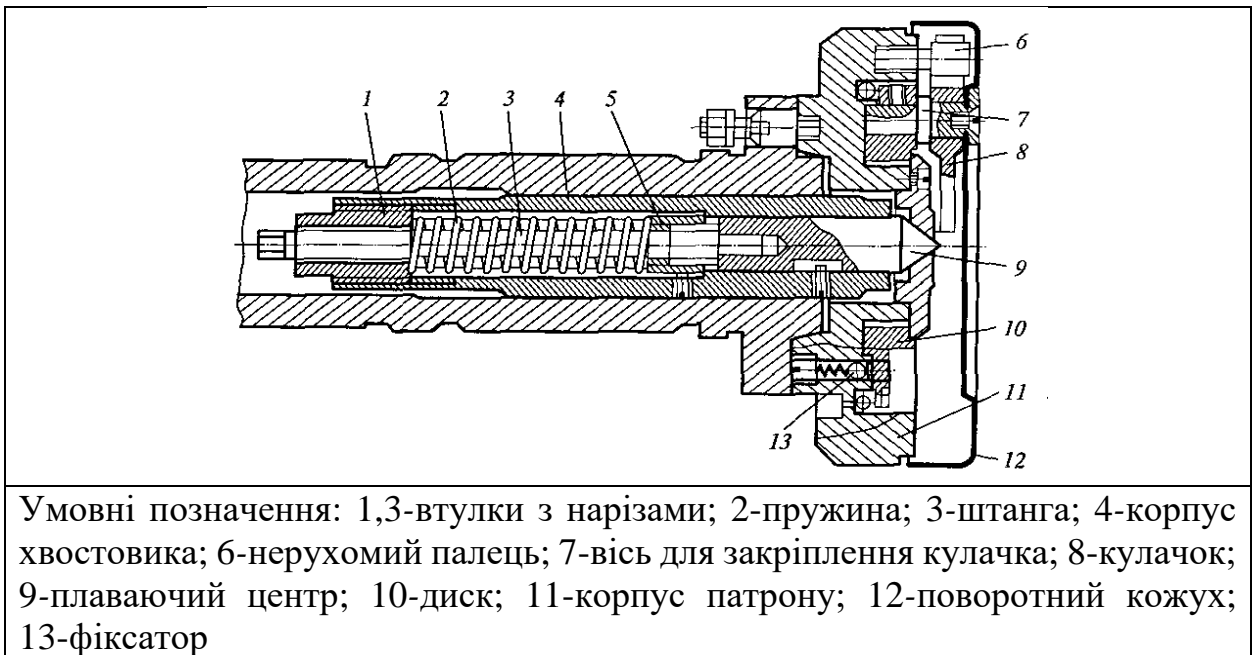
Універсальний повідковий патрон для базування деталей в центрах
